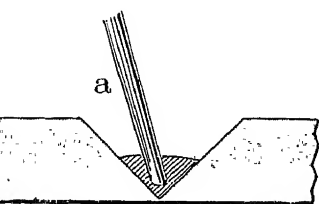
Soudure autogène de pièces épaisses d'aluminium. (*a*, métal d'apport.)
